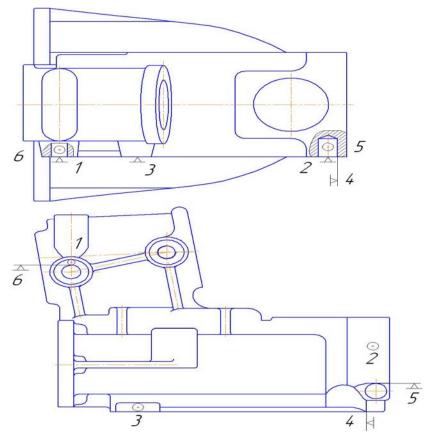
Схема базирования заготовки «Корпус редуктора»
